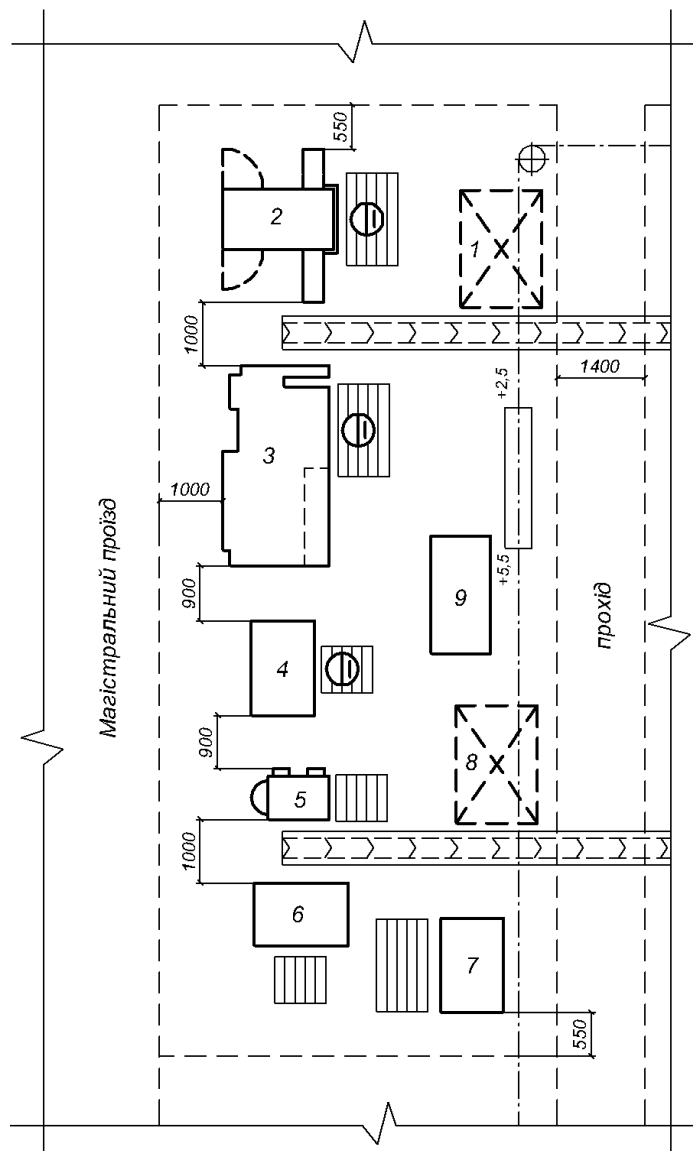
Планування розташування обладнання на ділянці механічної обробки деталі «корпус ПС-10А.43.005»:
